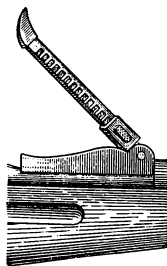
Секторный открытый прицел русской военной винтовки образца 1891—1930 гг.
